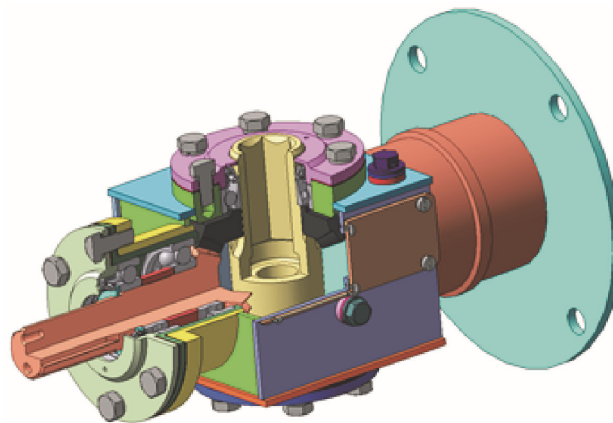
Цифровая 3D-модель сборочной единицы «Редуктор конический»
